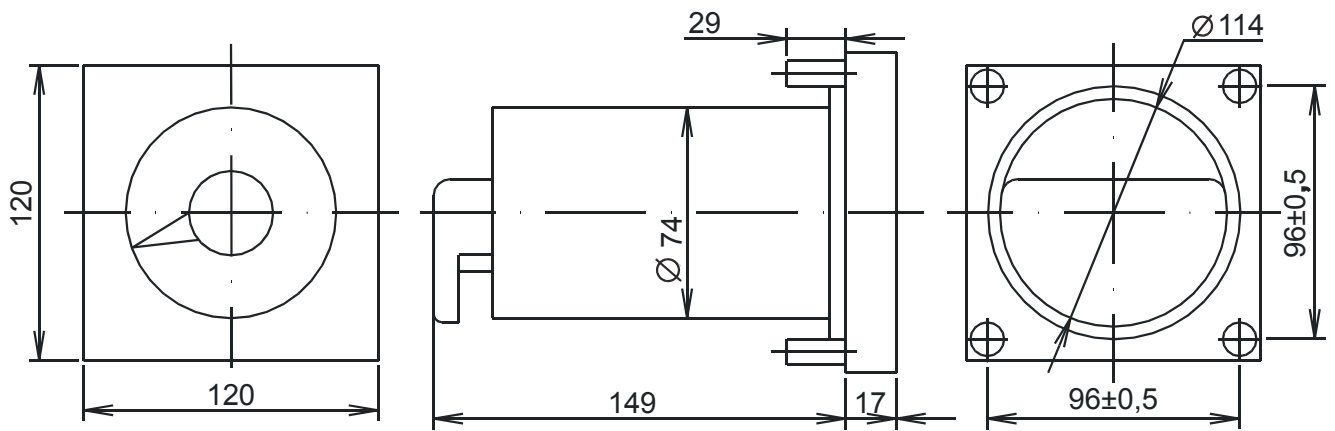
Габаритный чертеж приборов Ц1420 и Ц1420.1
